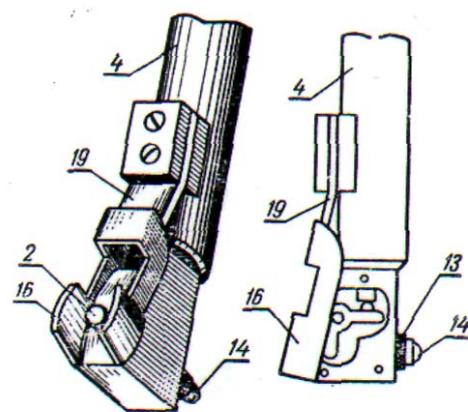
Корпус индикаторного нутромера для размеров от 18 до 35 мм: 19 – пружина
